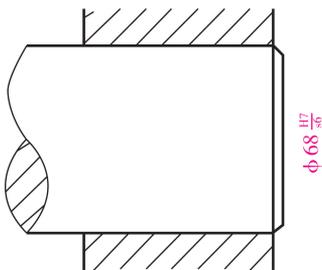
孔和轴的公差带在装配图上的标注
